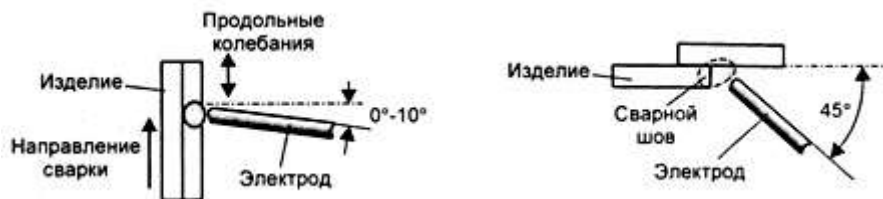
Положение электрода при сварке нахлесточного соединения в вертикальном положении снизу вверх.
